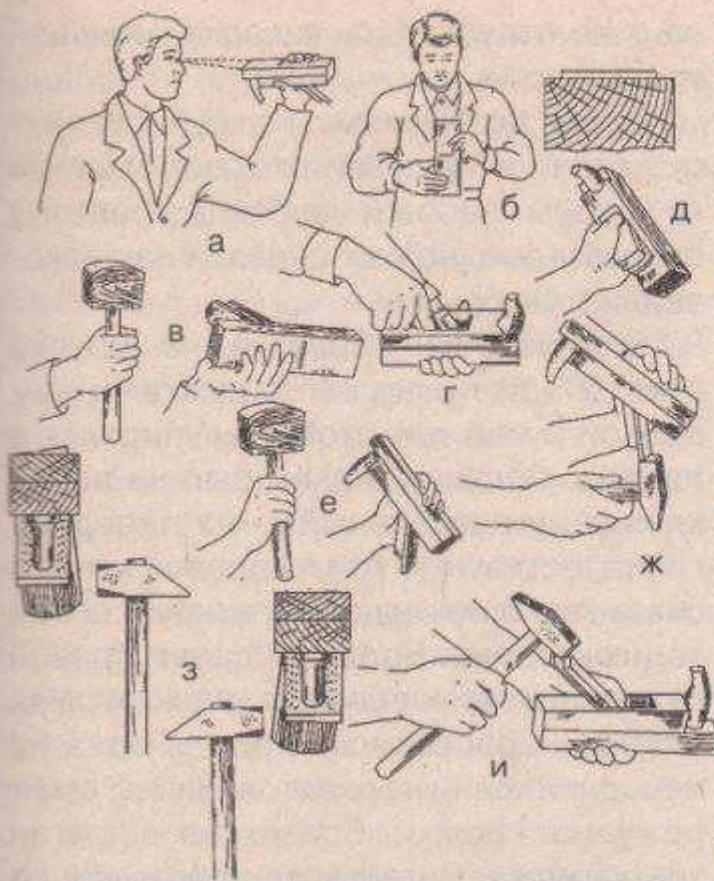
Наладка рубанка: а — проверка выпуска и остроты ножа; б — регулировка выпуска ножа; в — разборка с помощью удара; г — вытаскивание и установка ножа на основание (постель); д — приемы закрепления ножа; е — выпуск ножа ударом по колодке; ж — выпуск ударом по ножу; з — выпрямление перекоса ножа; и — закрепление ножа
